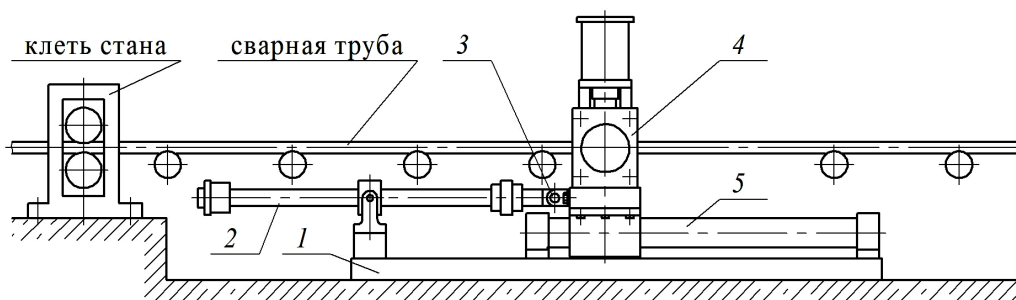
Структурная схема летучих ножниц трубосварочного стана
